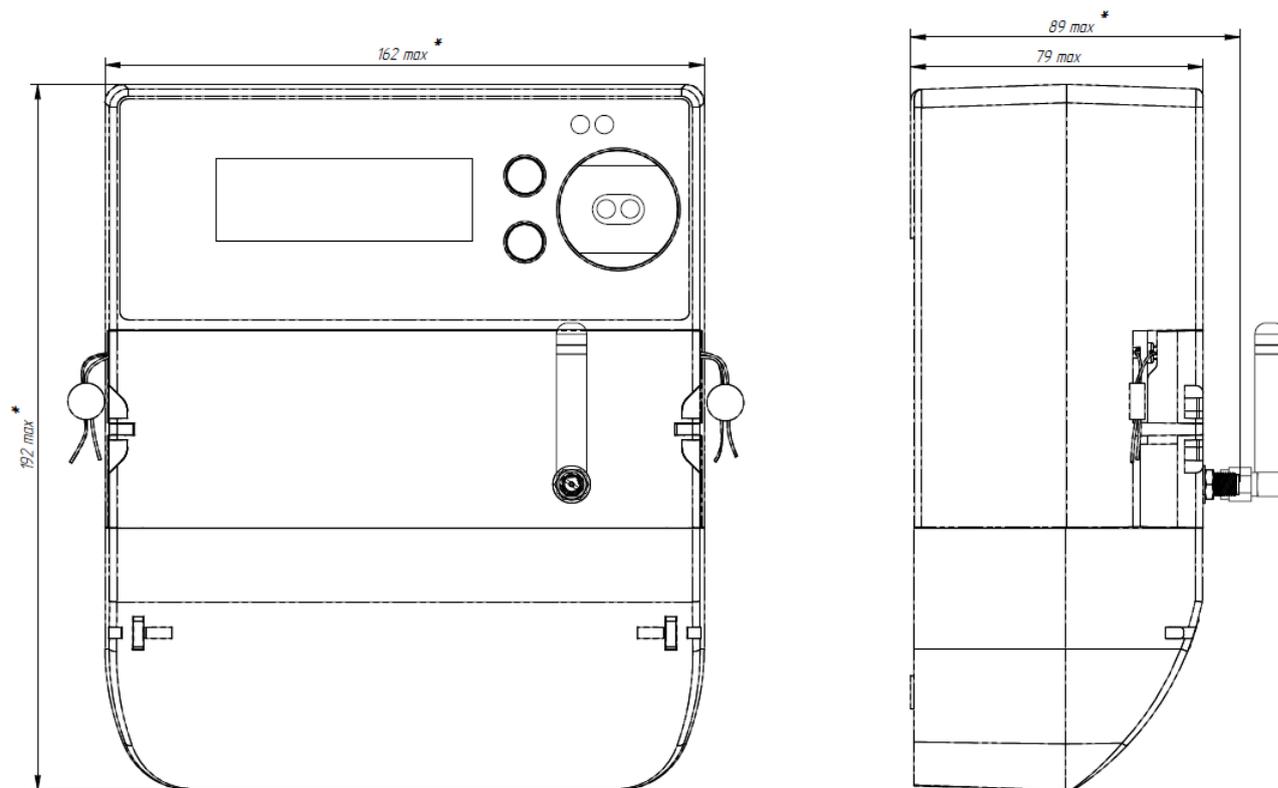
Габаритные размеры счетчика в корпусе 10м
